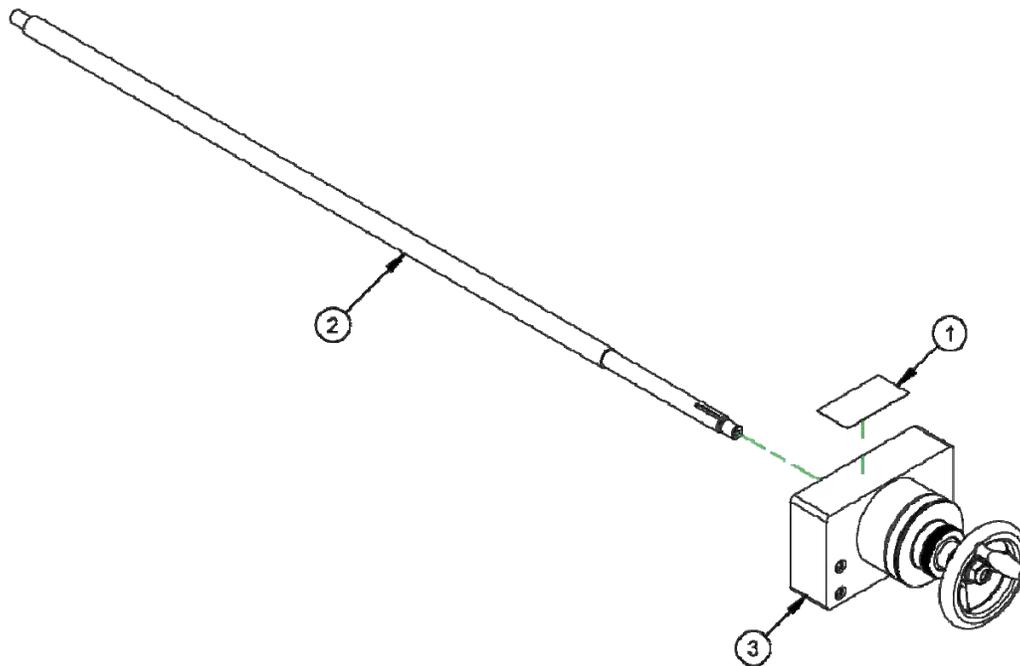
CONJUNTO CONTROLADOR 2 79218
